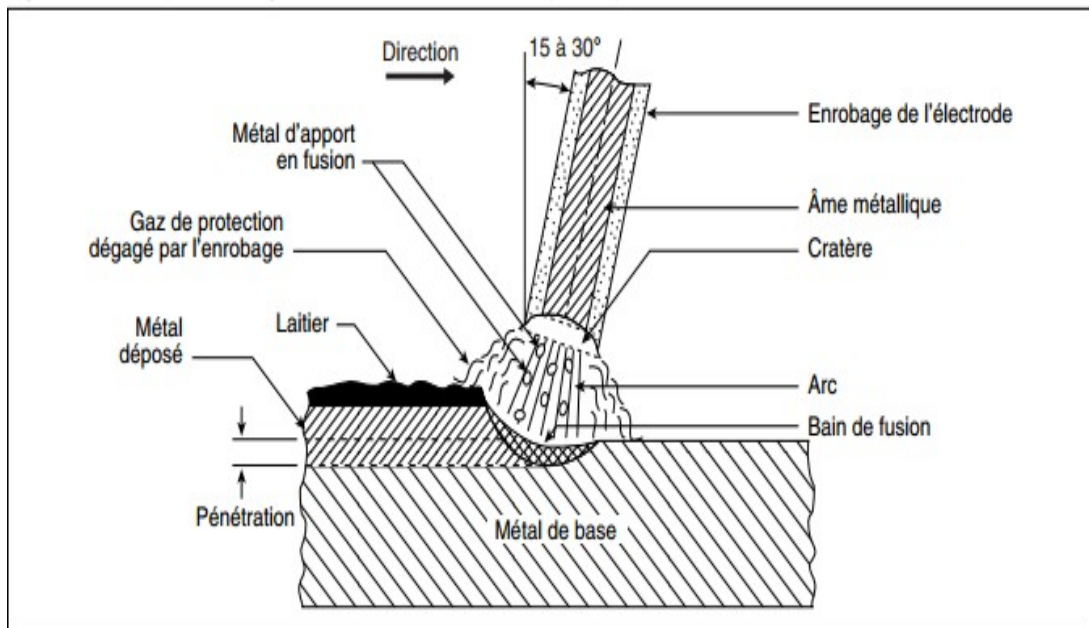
Le principe de procédé soudage SMAW.
